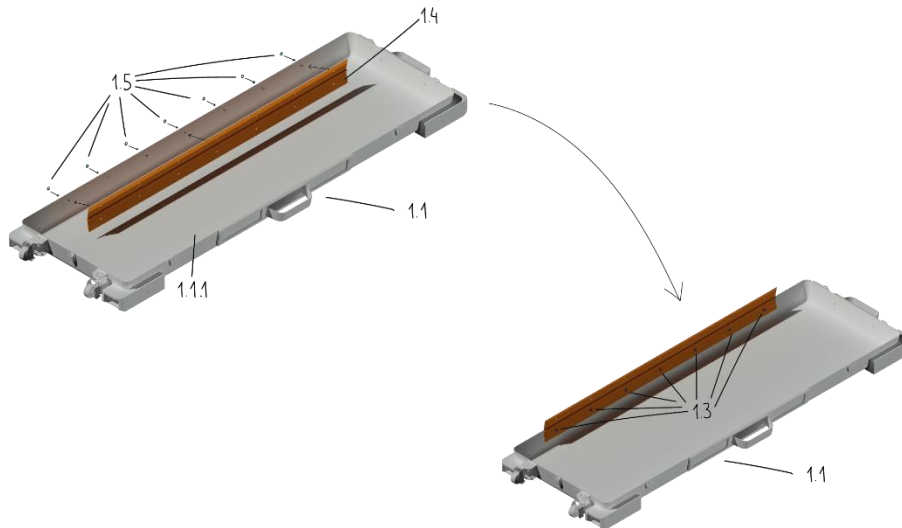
Ensamblaje subconjunto 1 (1)
